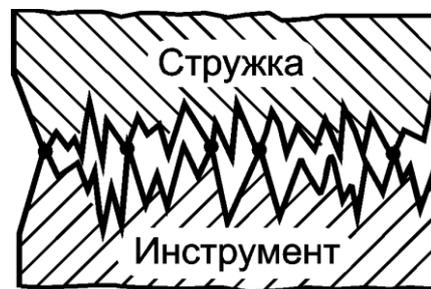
Схема образования «мостиков холодной сварки»
